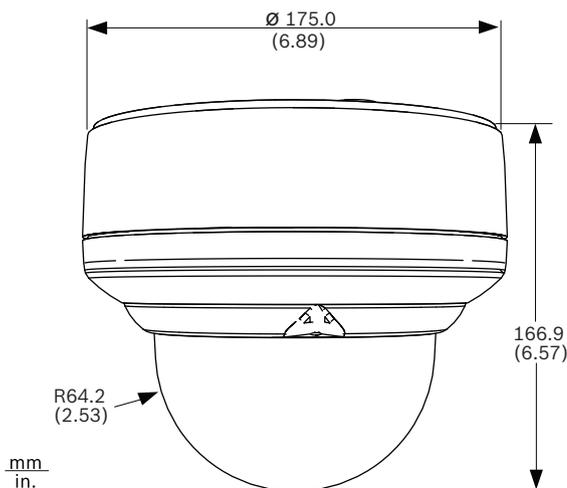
Dimensions du support de montage en surface pour l'intérieur
